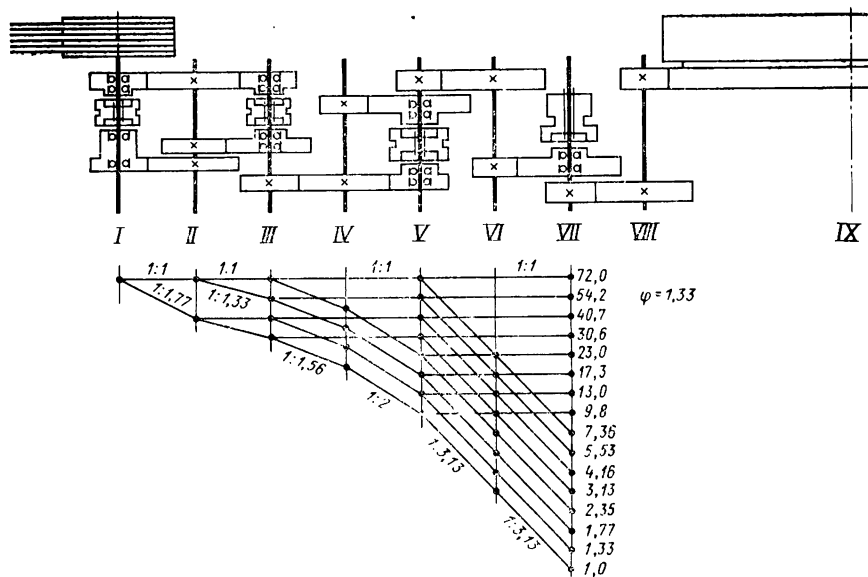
Схема коробки скоростей с переключением частот вращения планшайбы зубчатыми муфтами
